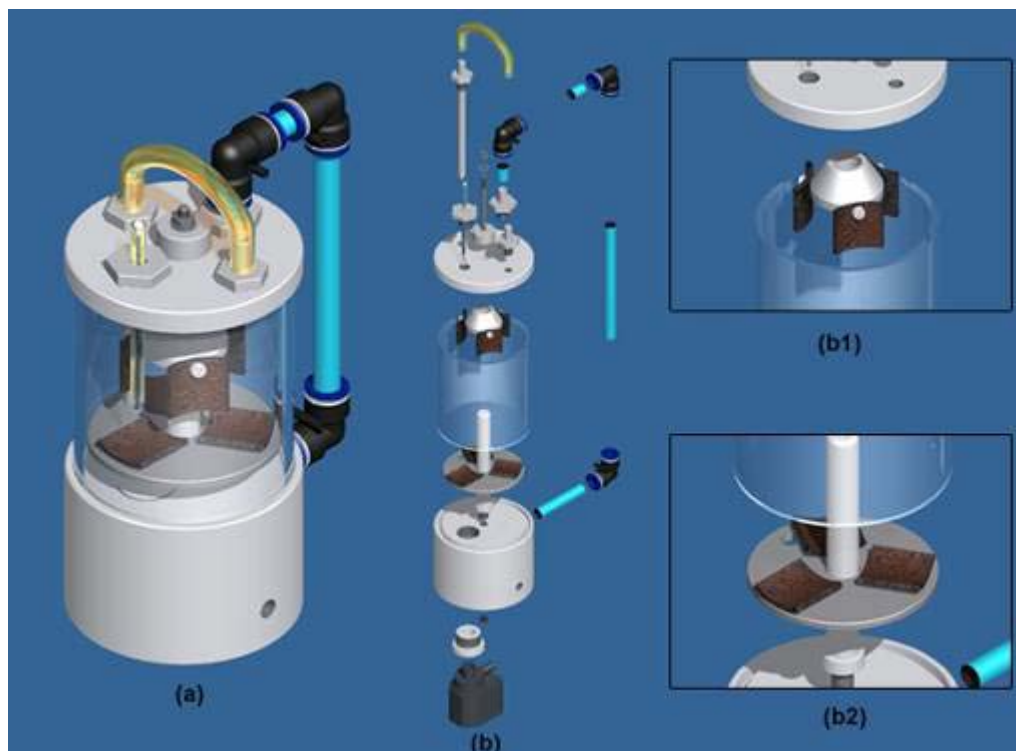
Desenho em perspectiva da célula de corrosão com agitação: (a) célula de corrosão montada, (b) vista explodida da célula de corrosão, (b1) detalhe dos corpos de prova na vertical e (b2) detalhe dos corpos de prova na horizontal.
